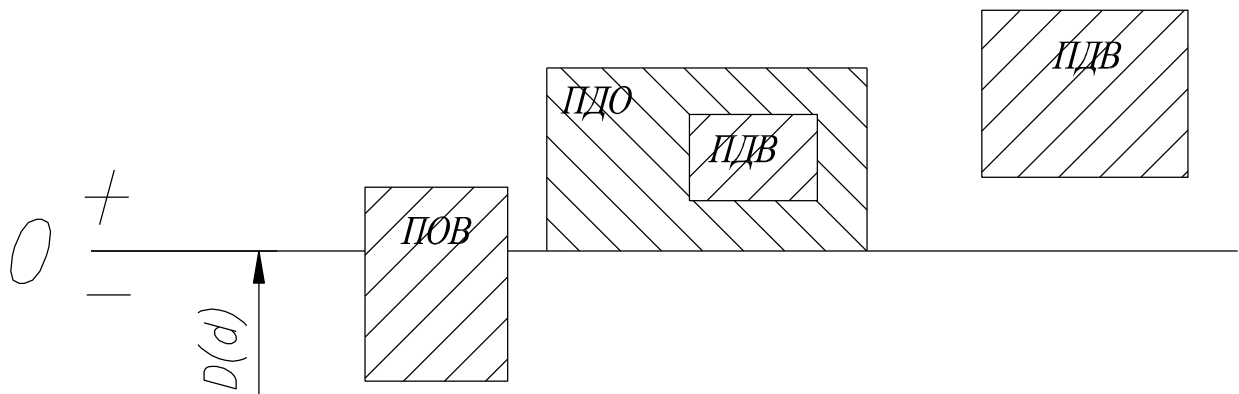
6. Схема розташування полів допусків перехідного з'єднання
